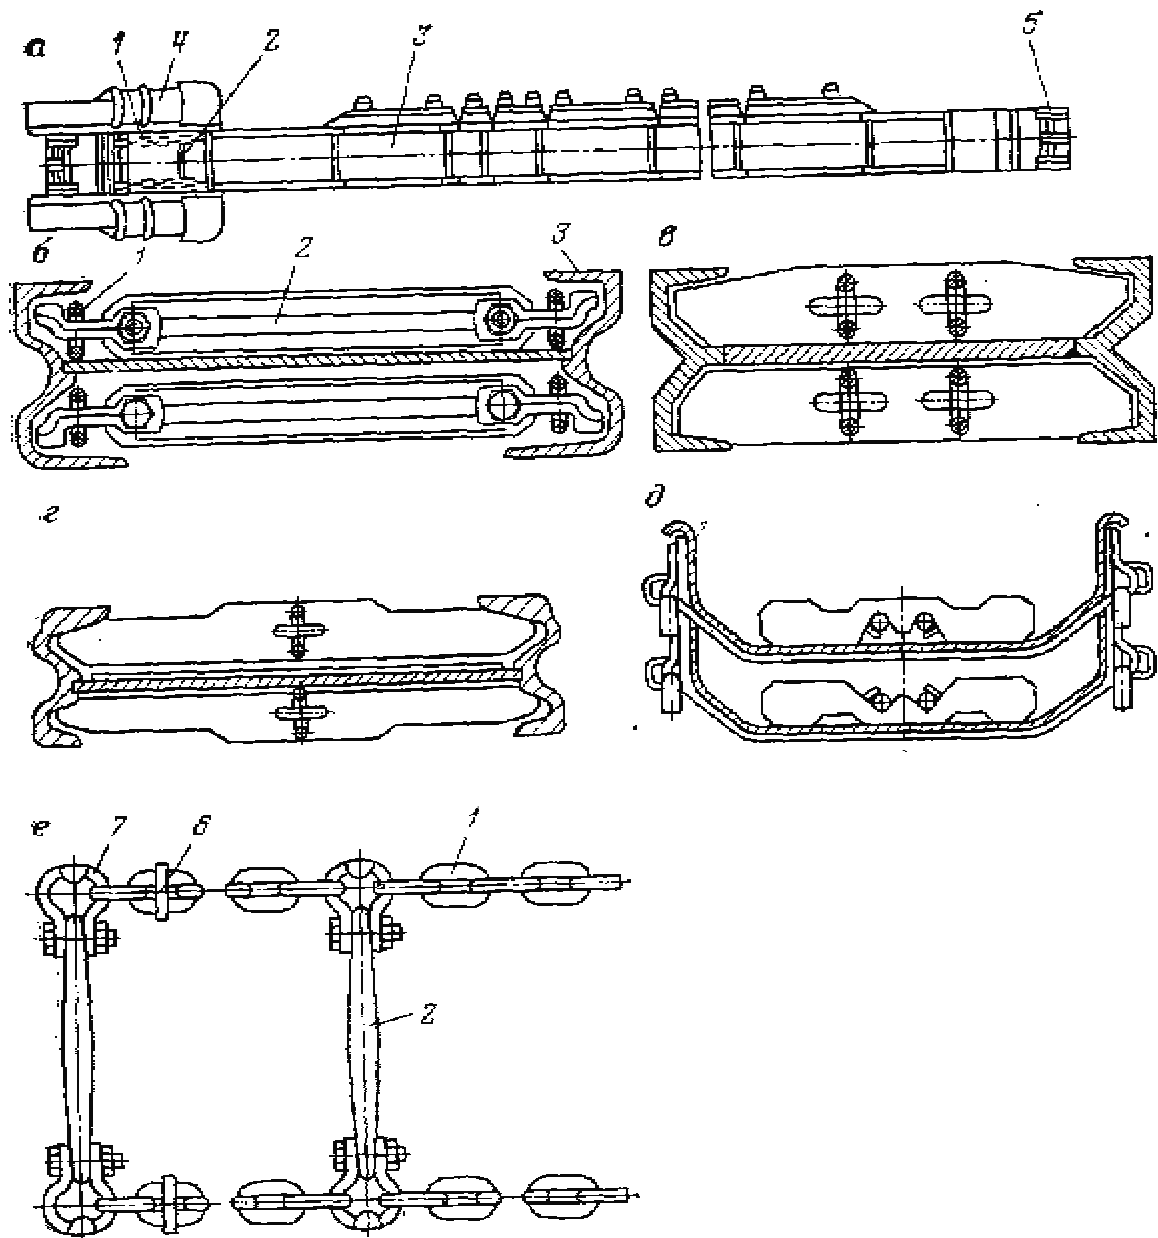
Скребокковый конвейер (а), конструкции решетчатого става (б-д) и тяговые цепи со скребками (е)
